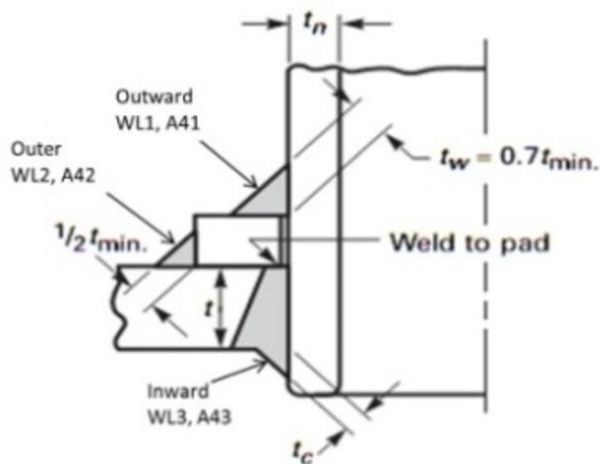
Ubicación de las piernas de soldadura, (ASME, 2013)
